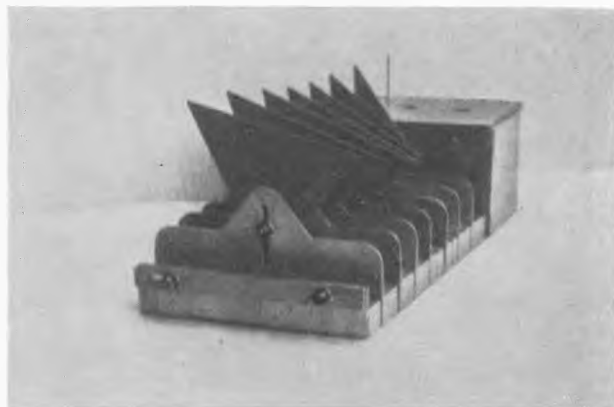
Für linksgängige Luftschrauben hergerichtet.
